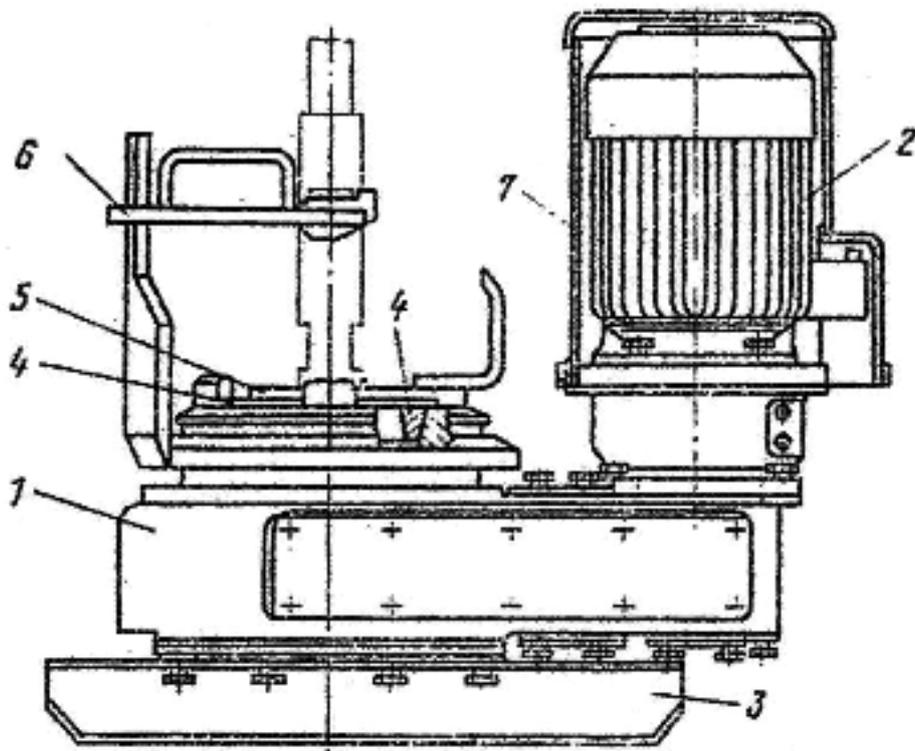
Труборазворот: 1 – станина; 2 – вращатель; 3 – водило; 4 – подкладная вилка; 5 – отбойная вилка; 6 – электродвигатель
